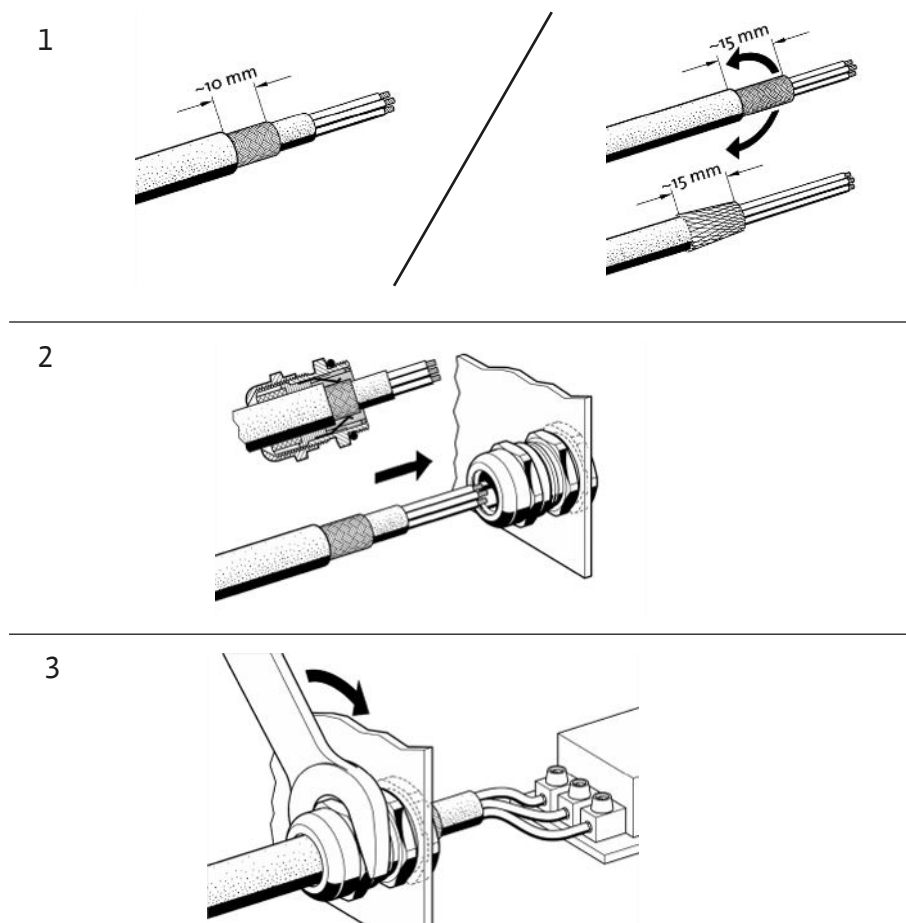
Pålegging av kabelisoleringer på EMC-kabelskjøter med gjenger
